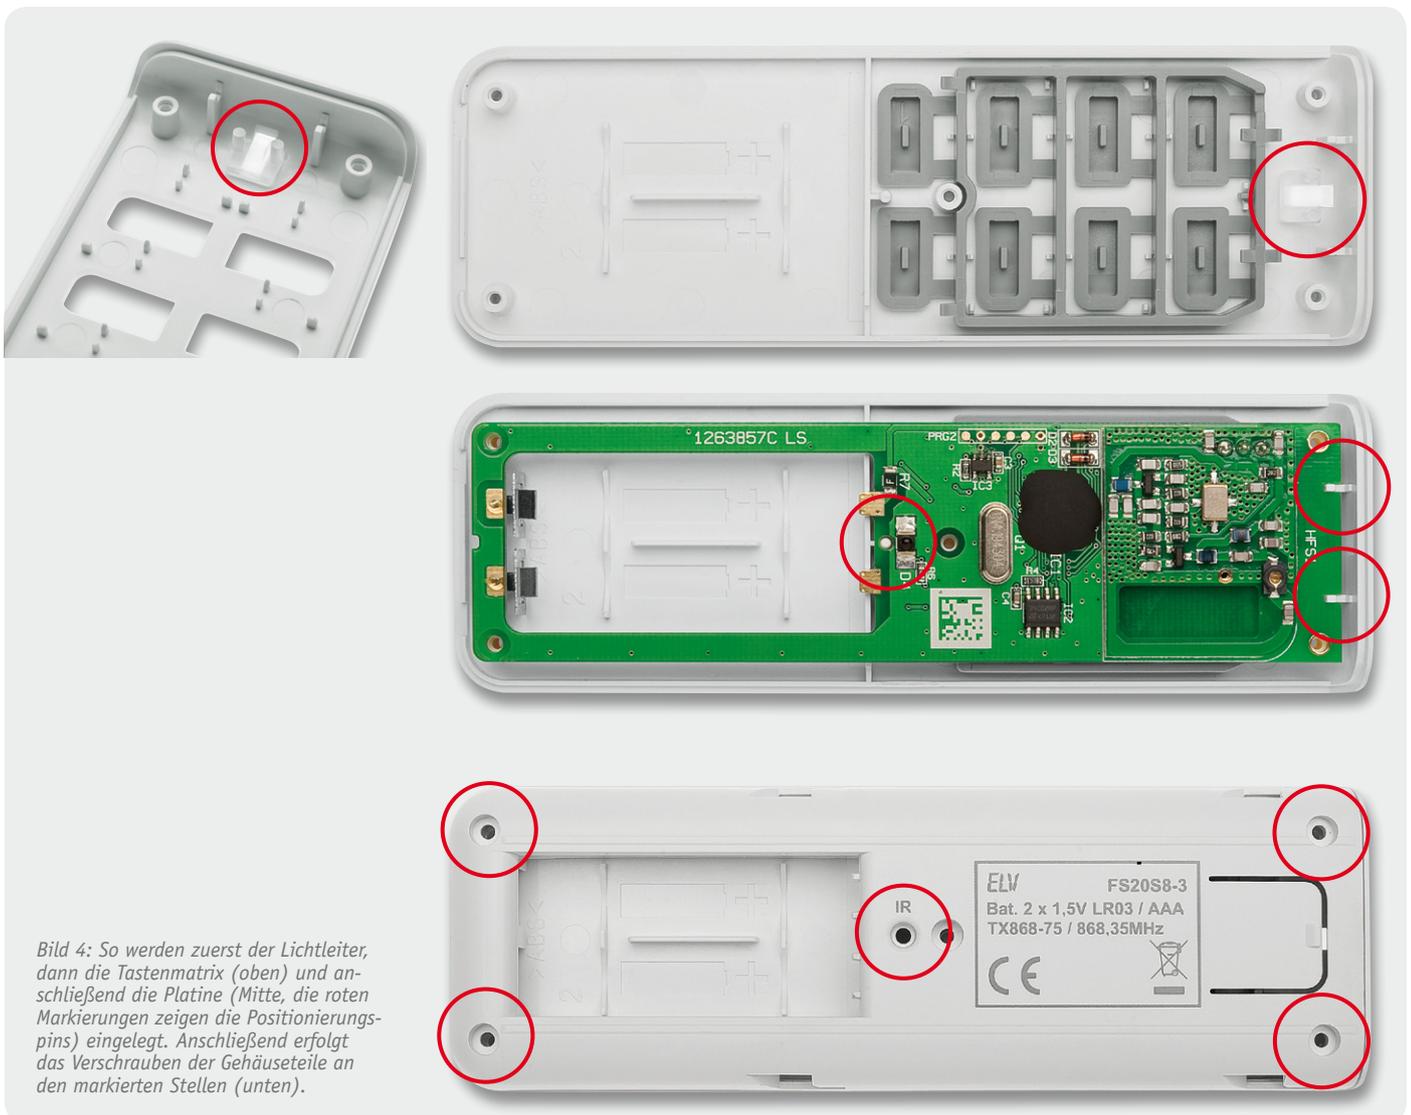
So werden zuerst der Lichtleiter, dann die Tastenmatrix (oben) und anschließend die Platine (Mitte, die roten Markierungen zeigen die Positionierungspins) eingelegt. Anschließend erfolgt das Verschrauben der Gehäuseteile an den markierten Stellen (unten).
